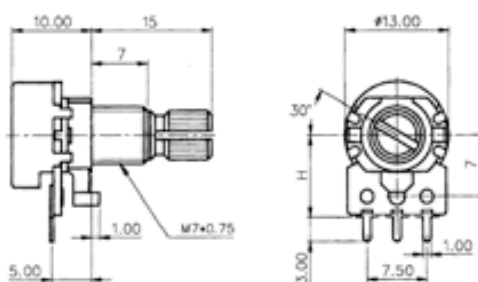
Габаритні розміри змінного резистора 16К1
